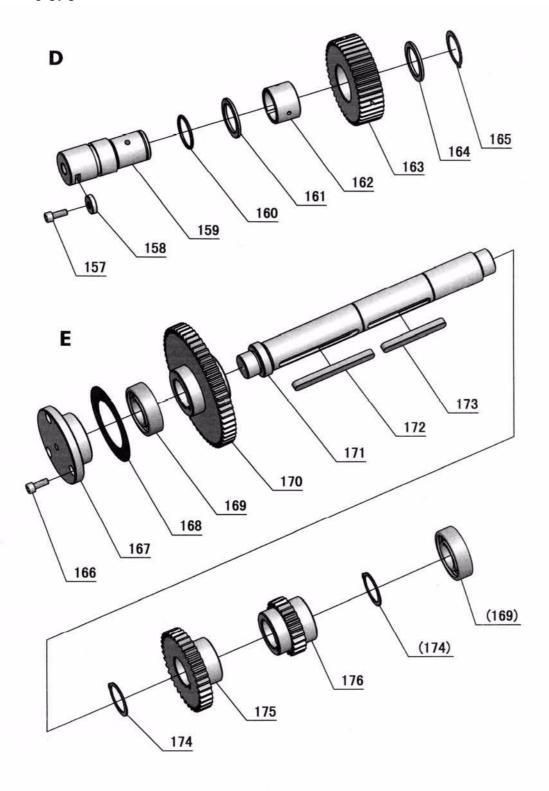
Spindelstock 6 von 8 - Headstock 6 of 8
